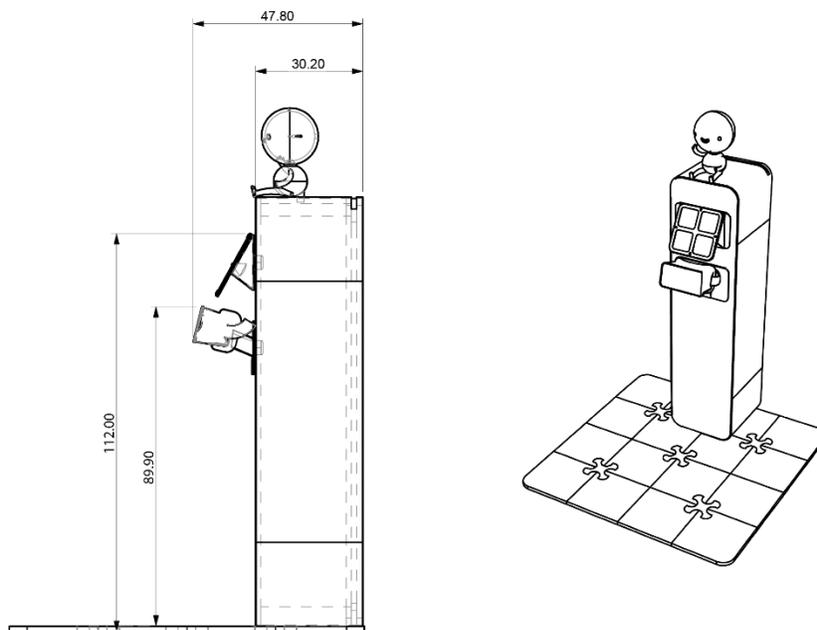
Plano General. Vista Lateral. 2018. Elaboración Propia
